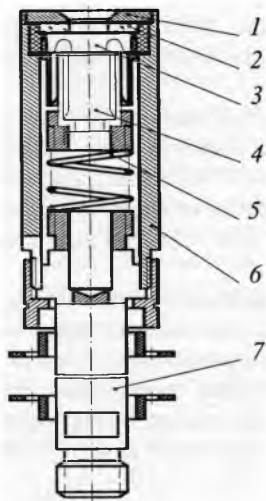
Схема головки Si(Li)-детектора: 1, 6 — крышка корпуса и корпус головки соответственно; 2 — сапфировое кольцо; 3 — Si(Li)-кристалл; 4 — блок полевого транзистора; 5 — пружина; 7 — медный хладопровод
